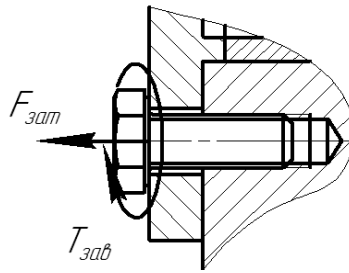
Соединение крышки подшипника с корпусом
